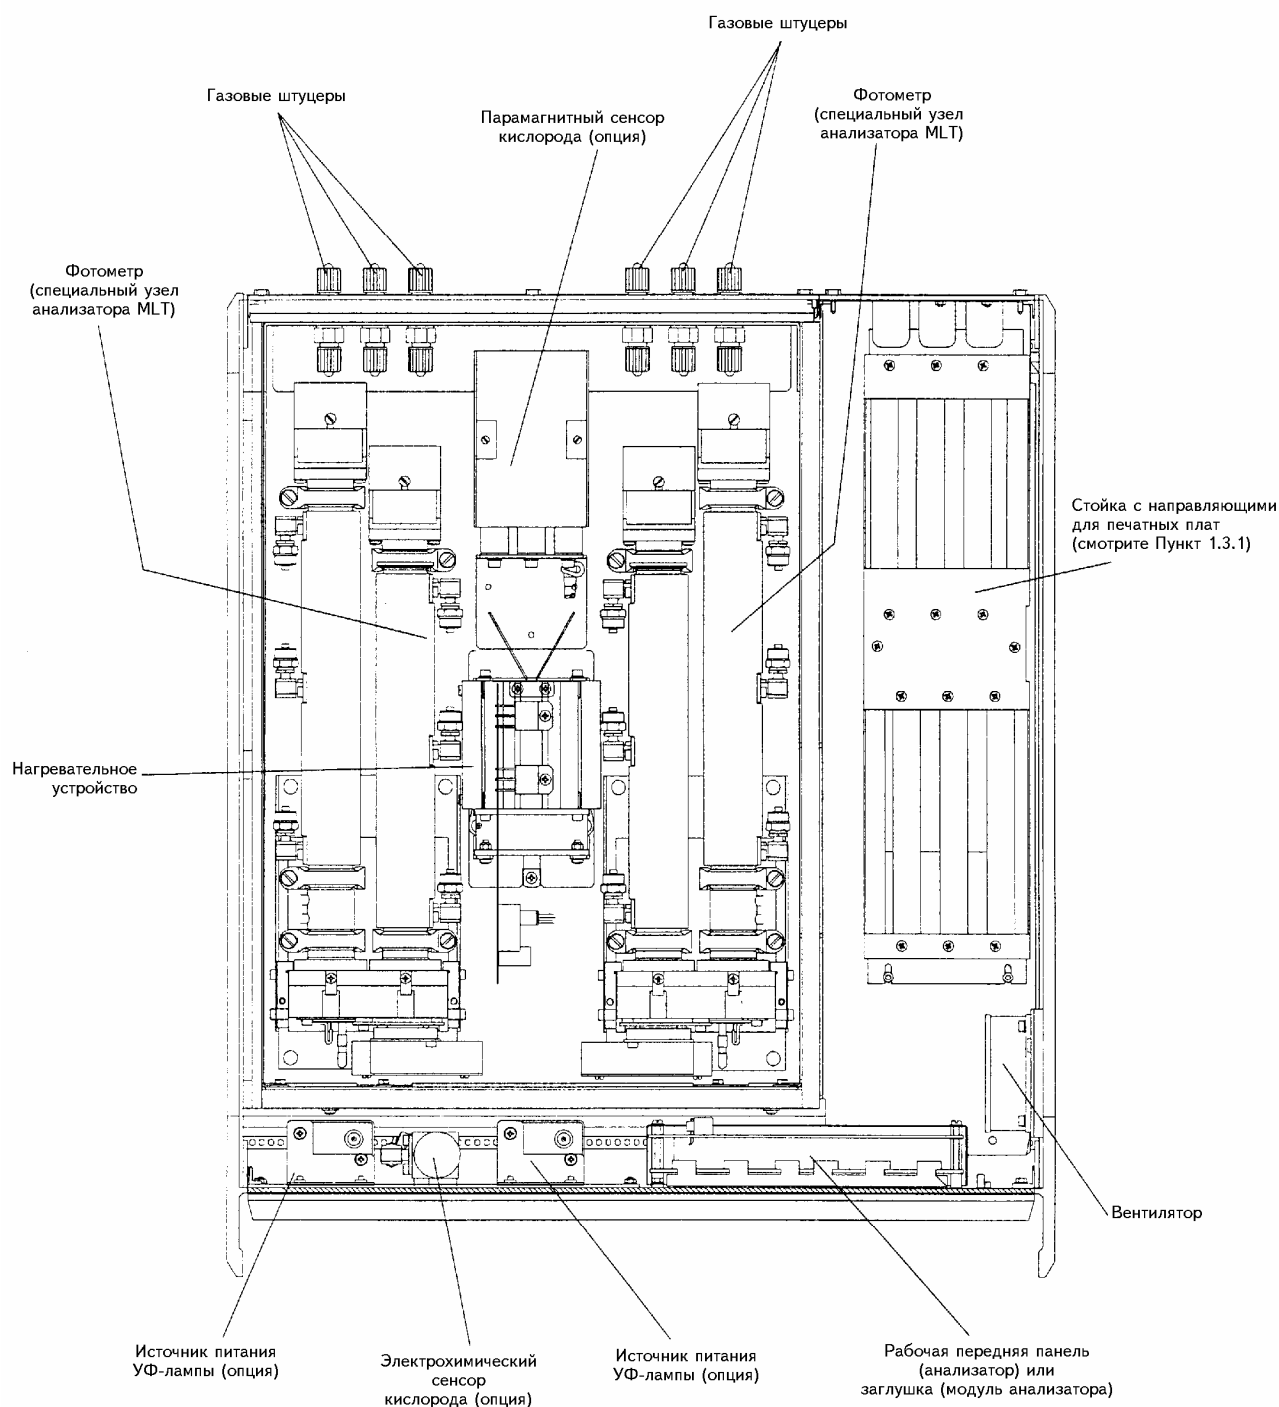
MLT 4, корпус для щита/стола, вид сверху
